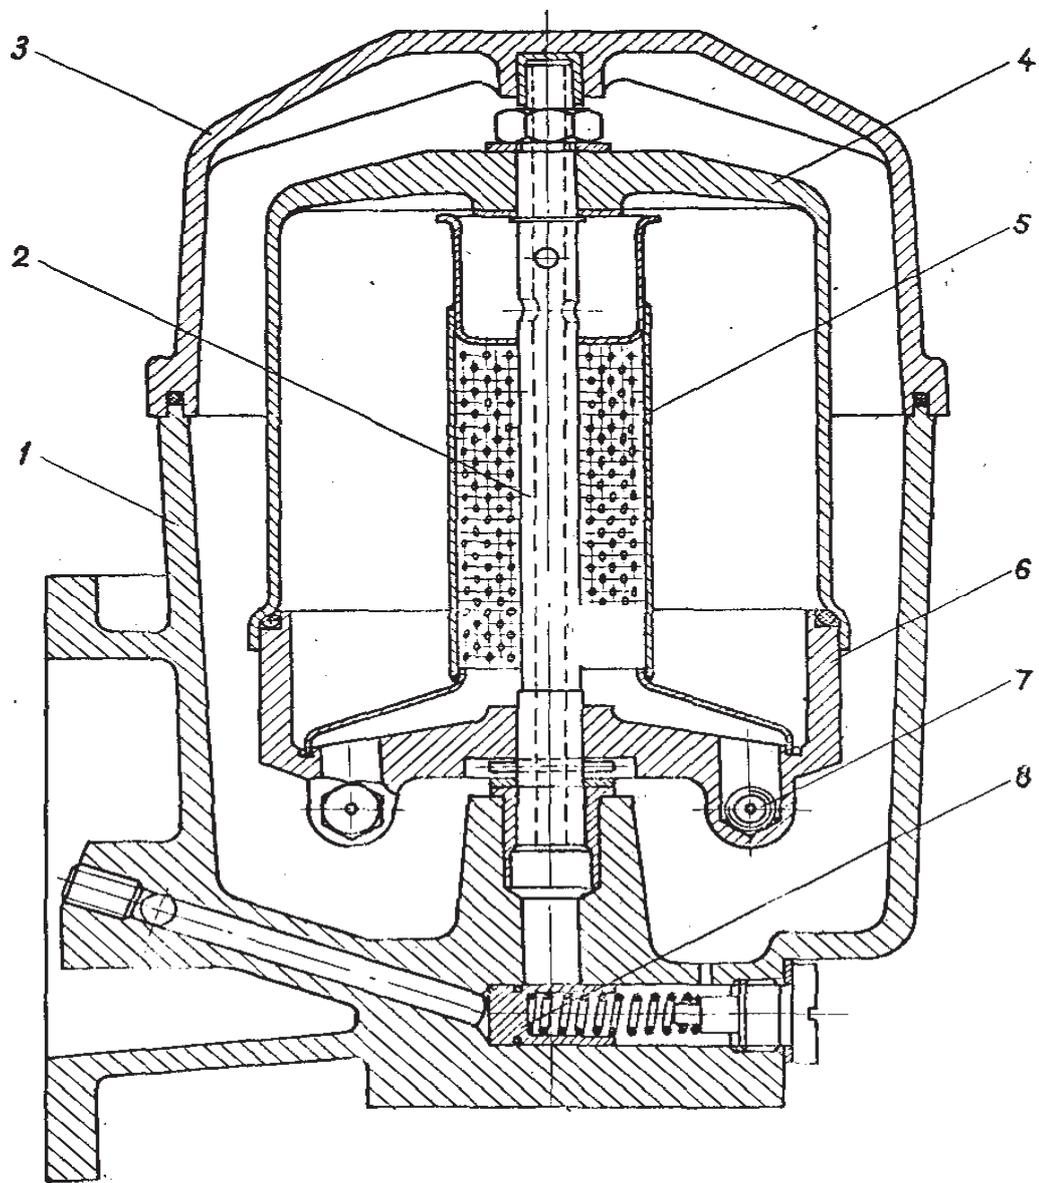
Центробежный маслоочиститель GF 238 двигателей 824TS
